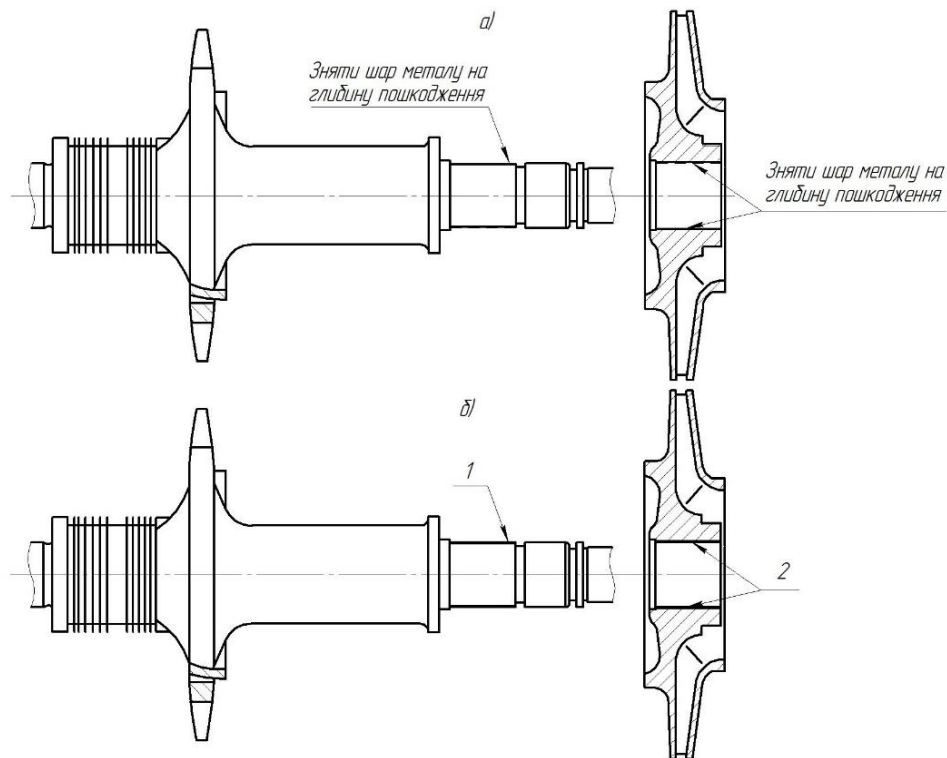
Відновлення посадки колеса компресорної частини турбокомпресора епоксидним адгезивом: а) підготовка поверхонь деталей перед відновленням; б) нанесення епоксидного адгезиву і посадка колеса компресора: 1 – вал ротора компресорної частини; 2 – робоче колесо компресора.
